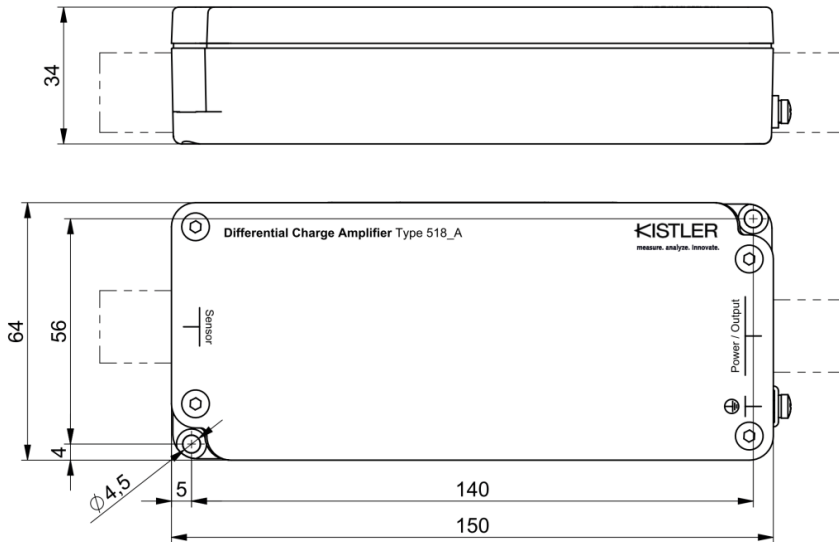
Dimensionen Typ 5181A... in Alu Druckguss Gehäuse Ausführung
